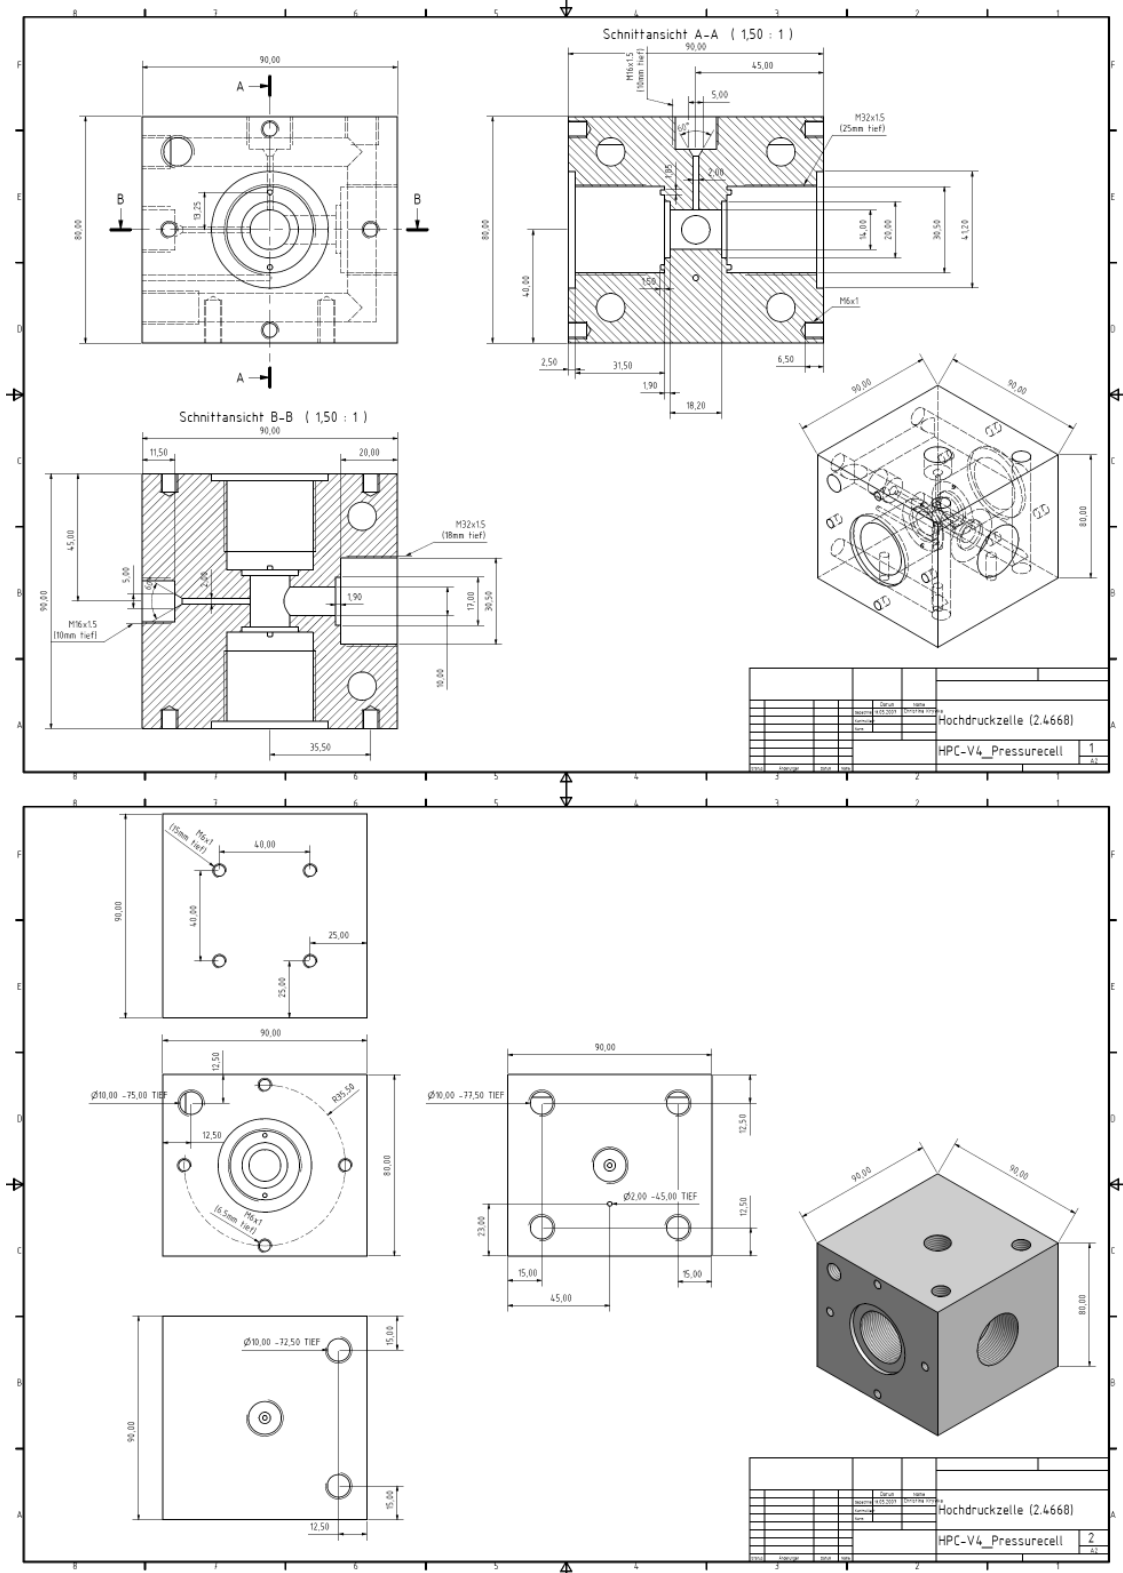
Technische Zeichnungen der Hochdruckzellenkomponenten
